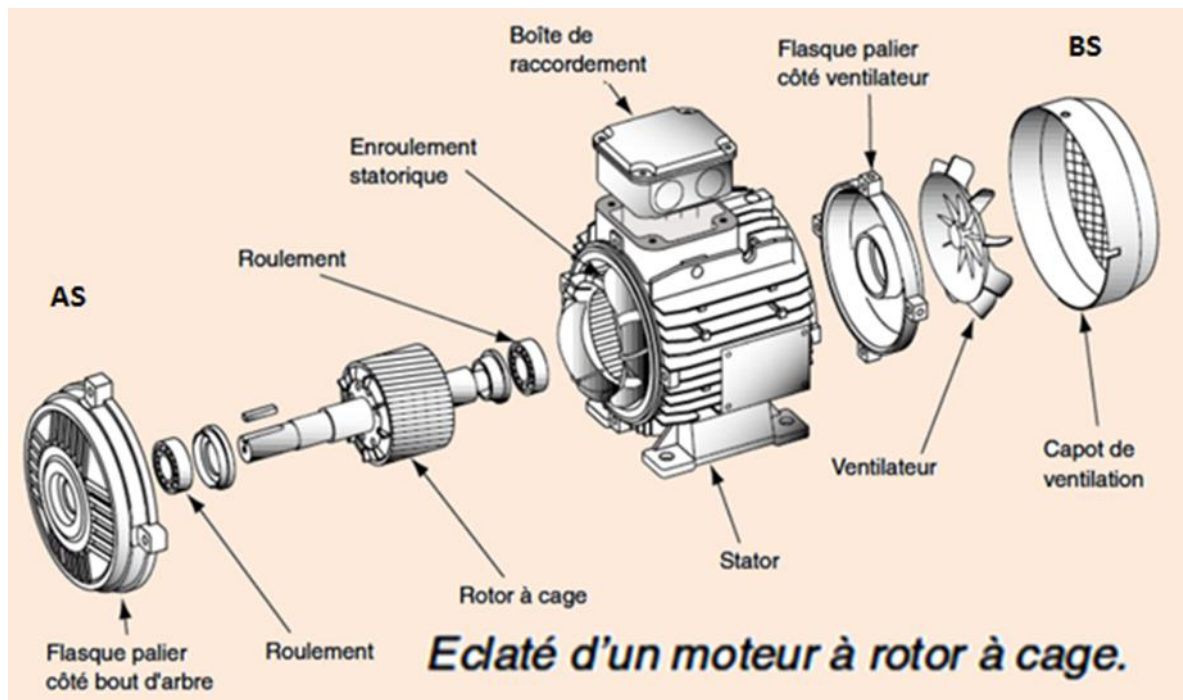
Forme éclaté d'un moteur à rotor à cage.
